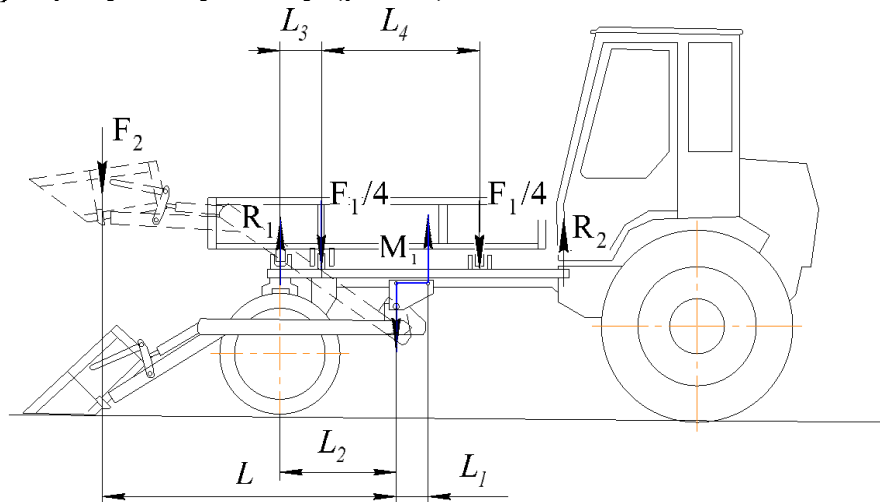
Розрахункова схема навантаження фронтального навантажувача
